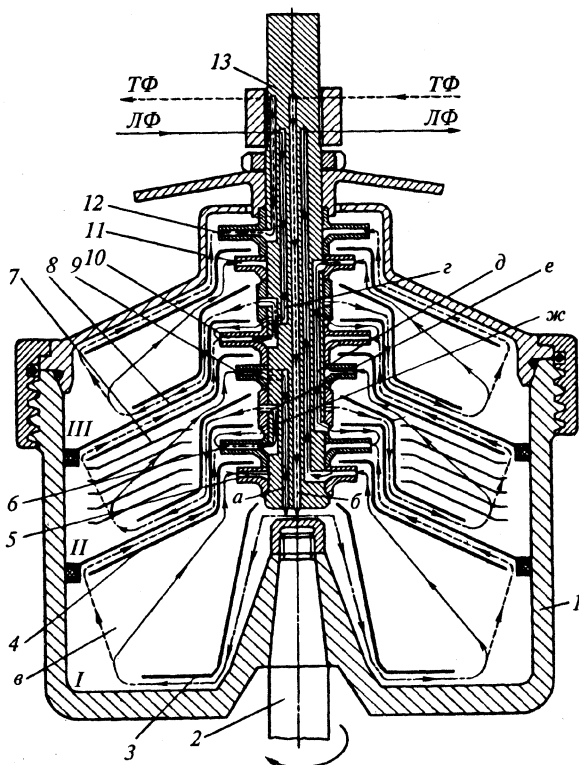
Трехступенчатый ротор типа «Лувеста»
